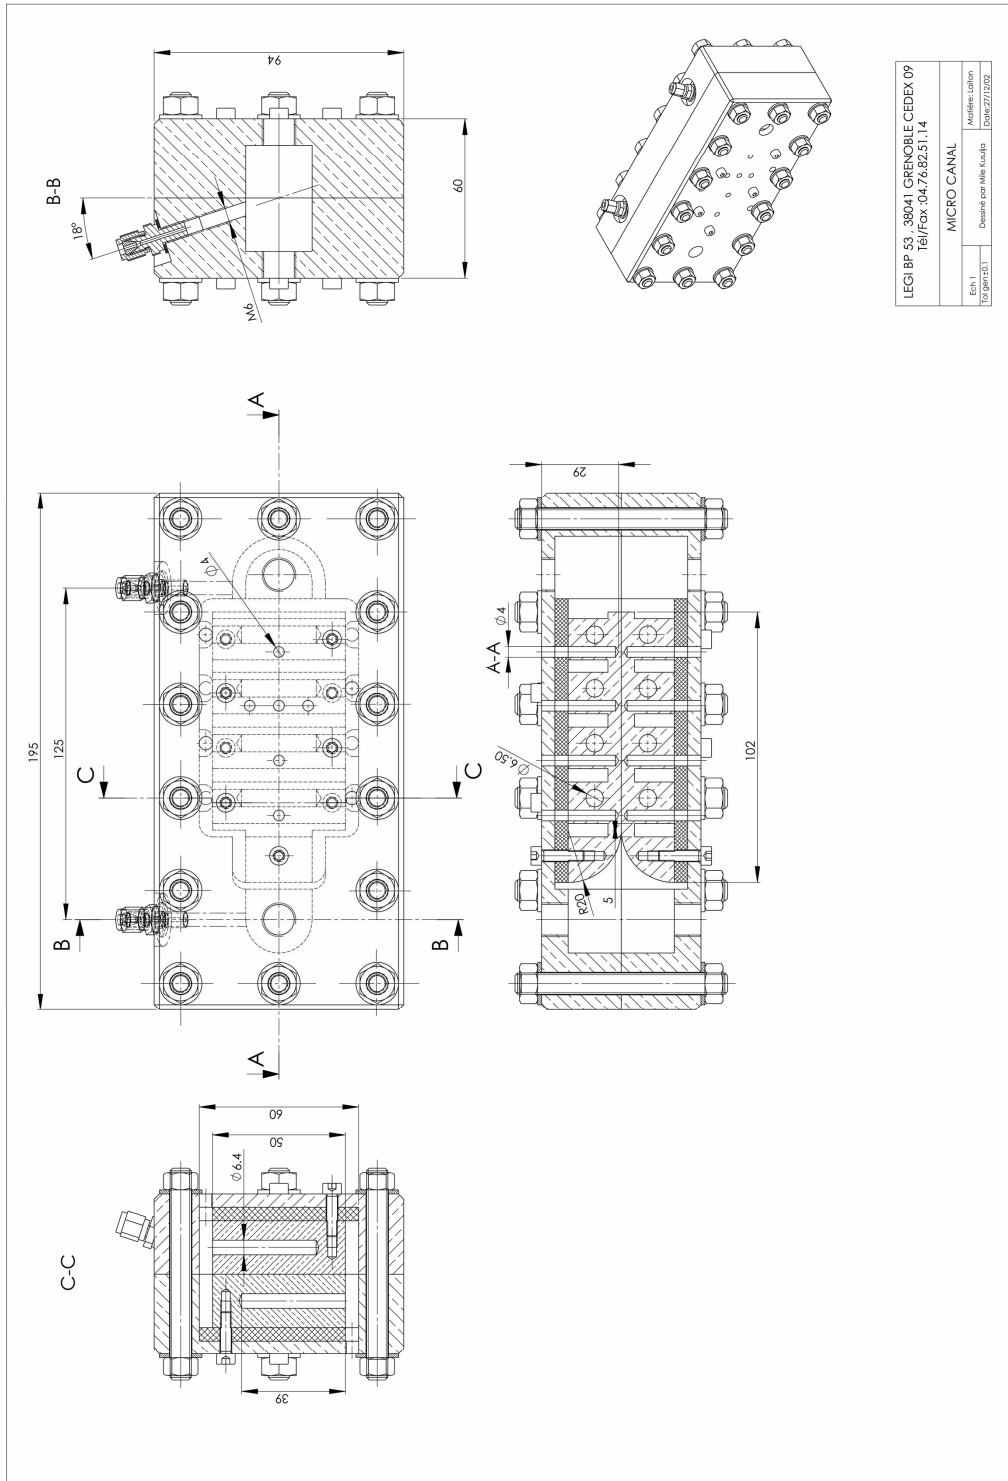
Section d'essais en laiton montée. Les coupes A-A et C-C font apparaître les plaques isolantes en verre époxy disposées entre le patin et la flasque.
